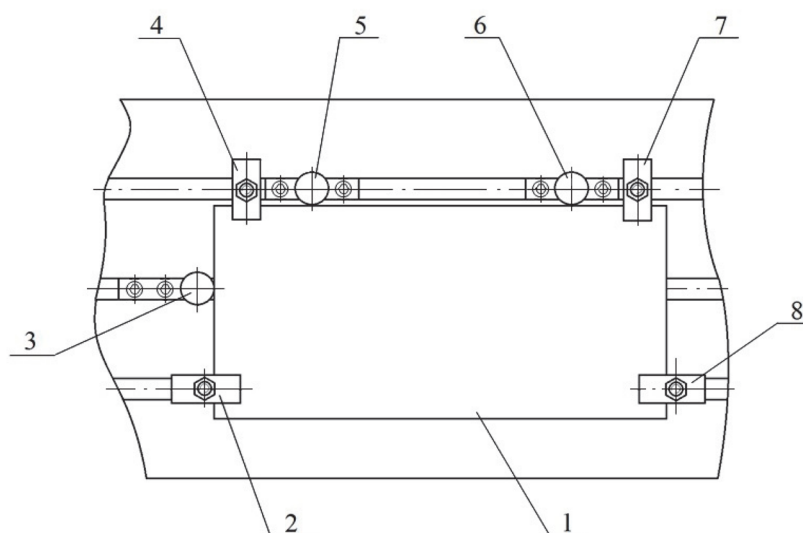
Базирование заготовки на столе станка с помощью съемных опор:
